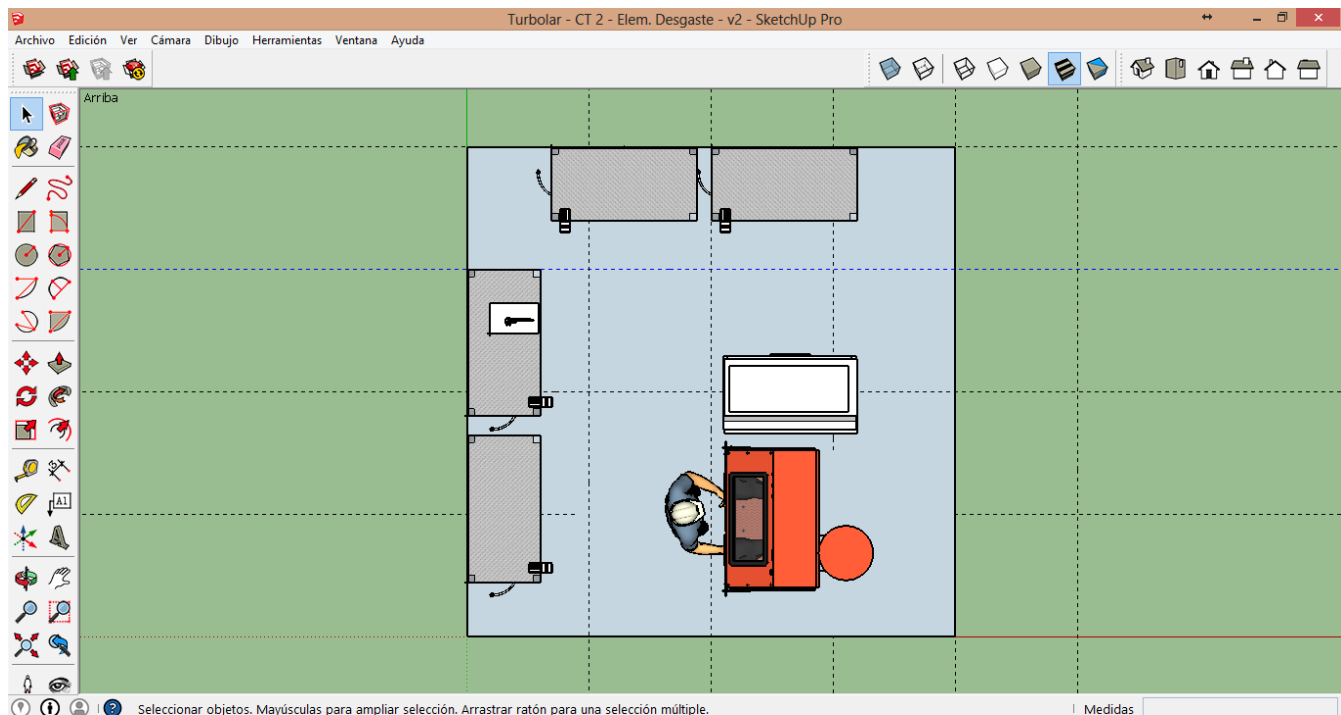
CT 2 – Elem. De Desgaste y Fijación – Vista Superior
